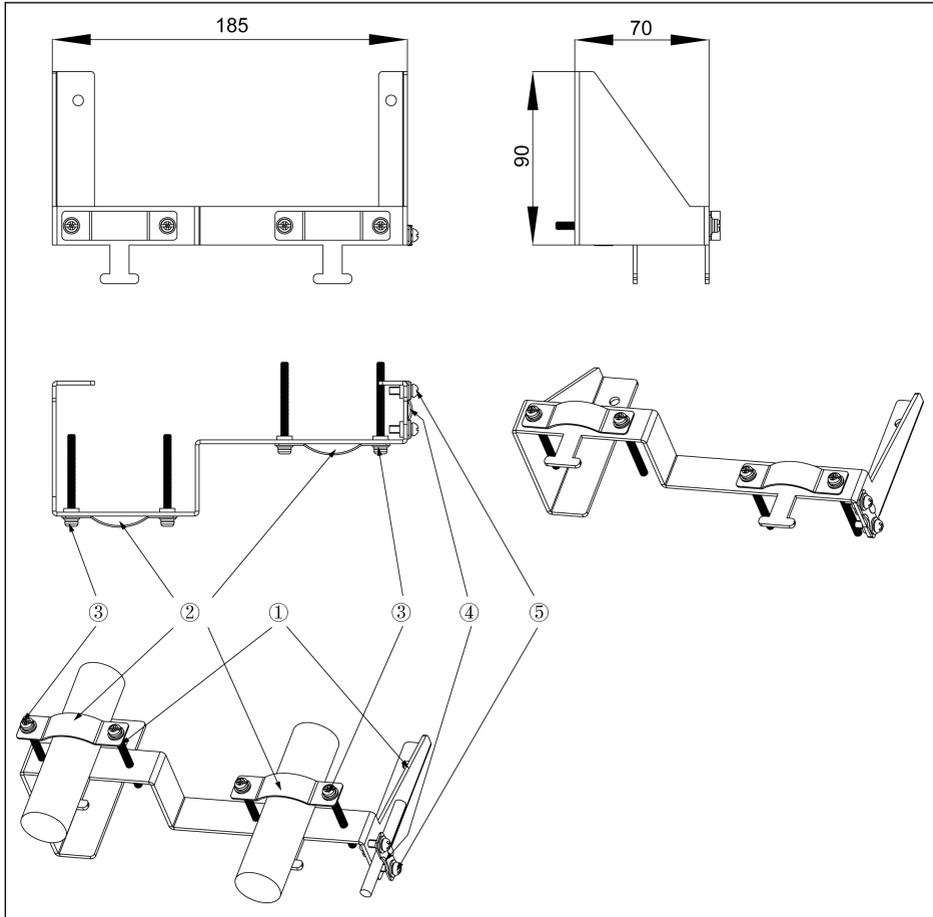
Conexión del cable apantallado con accesorios para 30K0...37K0
